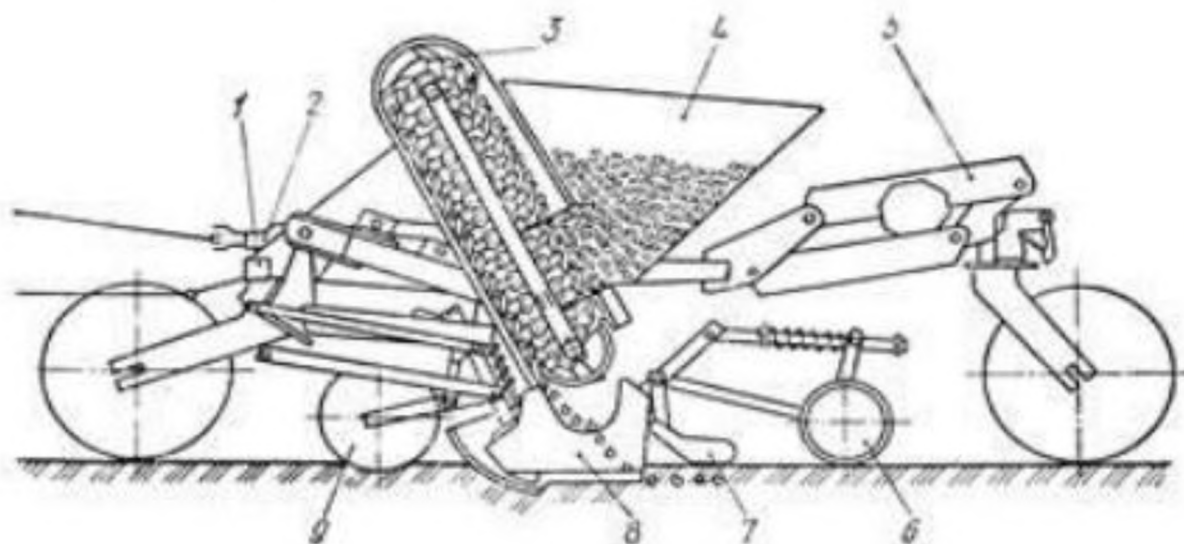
Схема сівалки точного висіву цибулі-сіянки СЛС-12: 1 – рама; 2 – механізм передач; 3 – висівний апарат; 4 – бункер для насіння; 5 – механізм підкочування; 6 – коток прикочування; 7 – загортач; 8 – сошник; 9 – коток копіювальний
